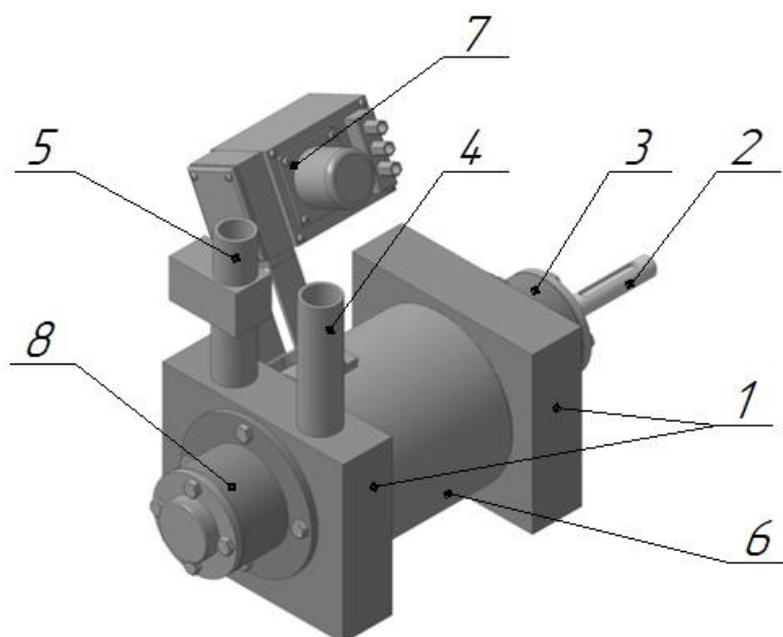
Конструкция ЖВН с устройством автоматического регулирования нагнетательного окна: 1 – лобавины; 2 – вал; 3, 8 – подшипниковые опоры; 4 – впускной патрубок; 5 – выпускной патрубок; 6 – корпус; 7 – нагнетательное устройство.
